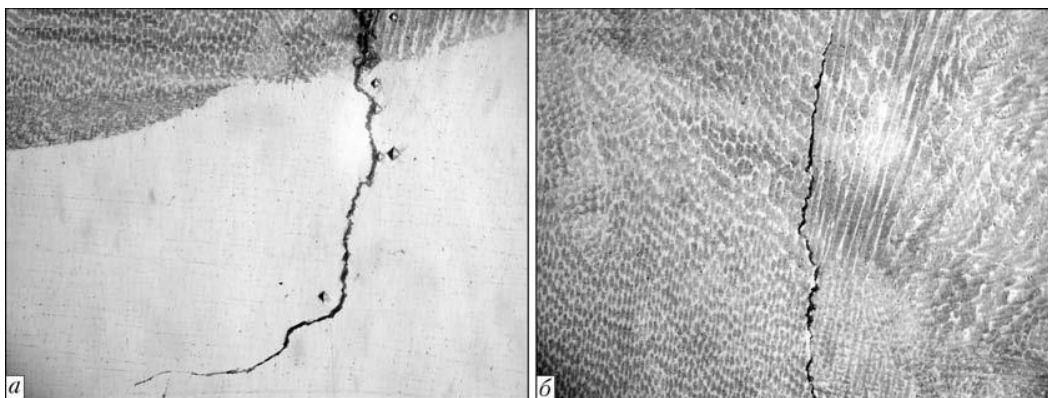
Образование горячих трещин при сварке плакированных сталей: в зоне сплавления подслоя и несущего шва
